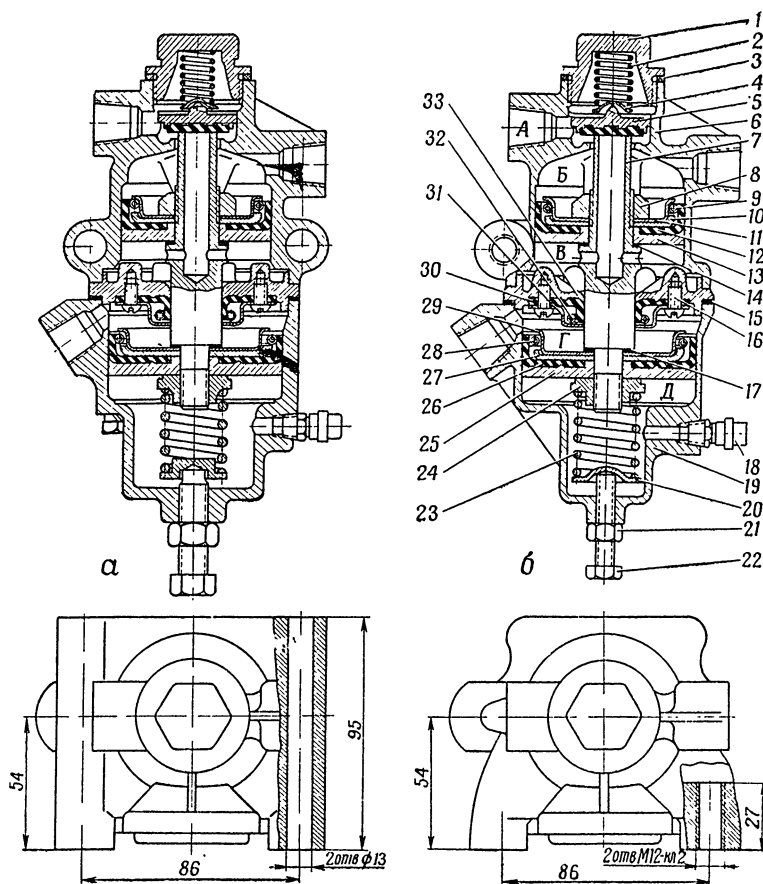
Конструктивная схема клапана управления тормозами прицепа автомобилей ЗИЛ
